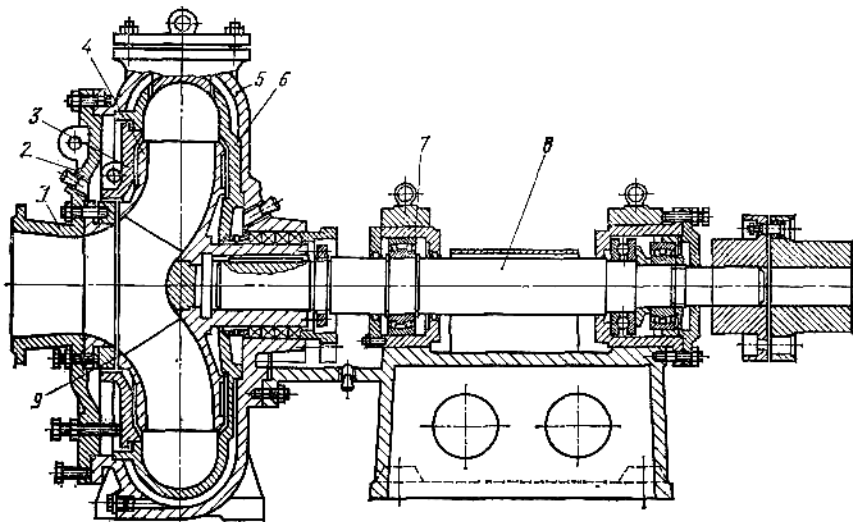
Типовая конструкция грунтовых насосов: 1 – всасывающий патрубок; 2 – крышка; 3 – бронедиск со стороны входа; 4 – рабочее колесо; 5 – наружный корпус; 6 – внутренний корпус; 7 – опорный узел; 8 – ротор; 9 – уплотняющее кольцо
